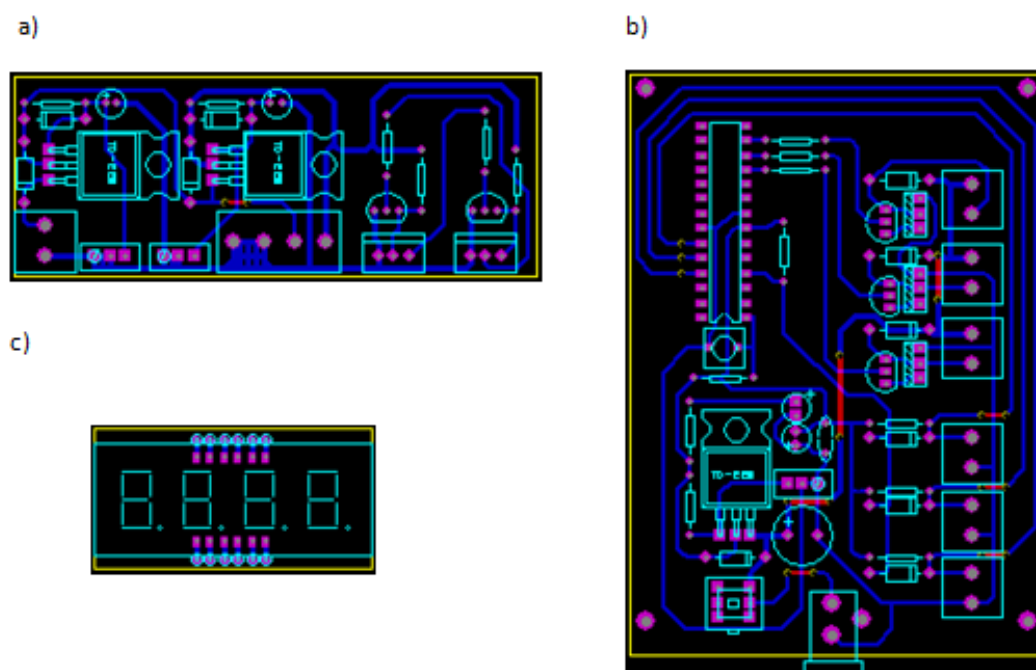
PCB De Los Circuitos: a) PCB De Las Fuentes De Alimentación, b) PCB Del Taxímetro y c) PCB De Los Displays De Tarifación. AUTOR.
